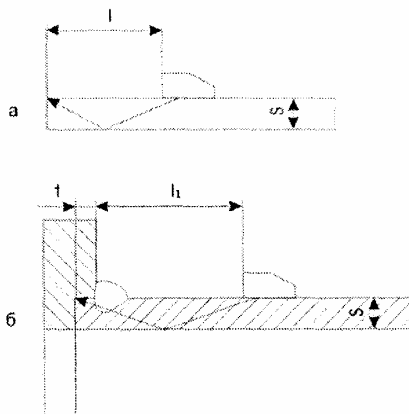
Схема измерения величины углубления штуцера при контроле угловых сварных соединений
